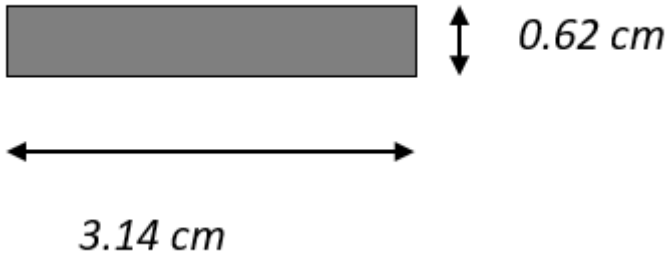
Sección transversal de la barra metálica Tipo 01
